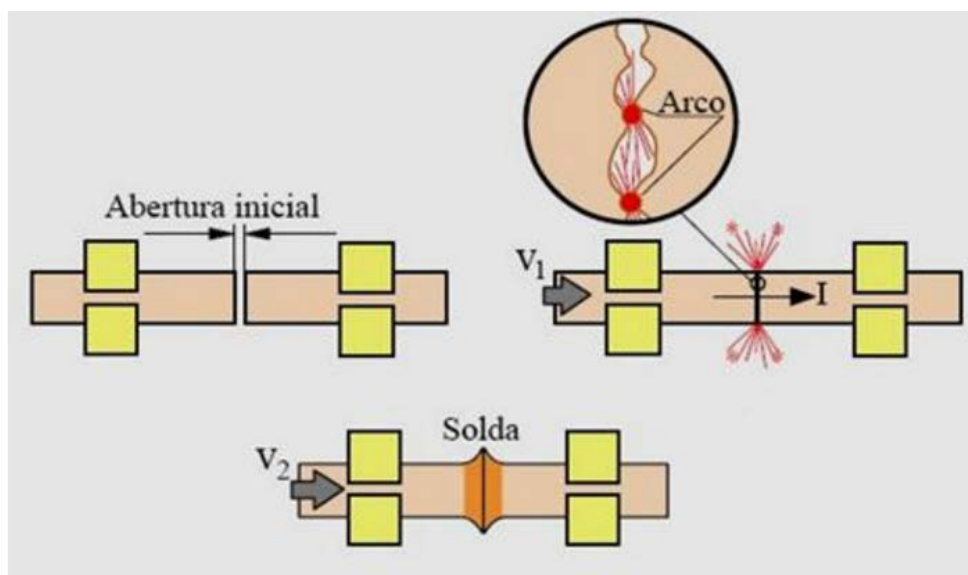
Tipo de soldagem por pressão, soldagem por centelhamento [52]
